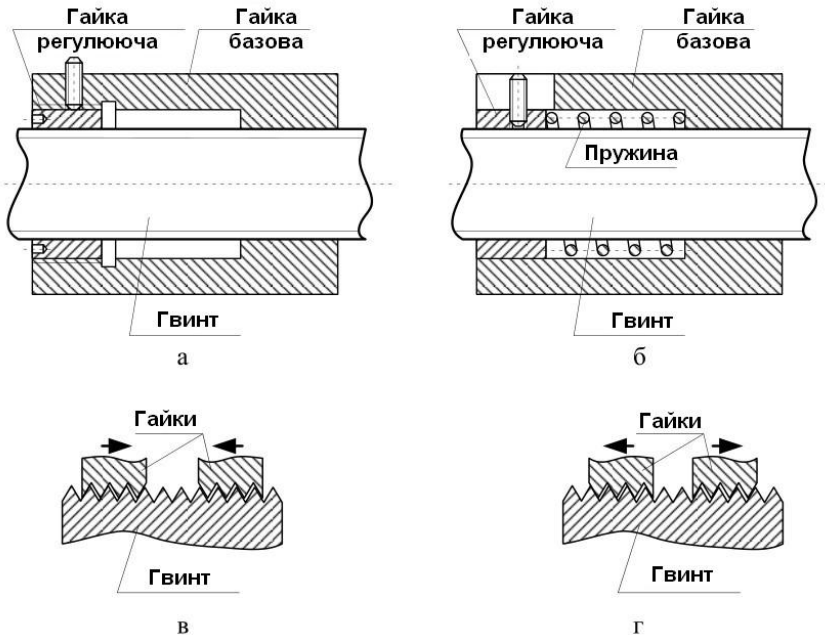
Схема люфтоусуваючого механізму на основі гайки із твердим і пружним регулюванням осьового зазору
